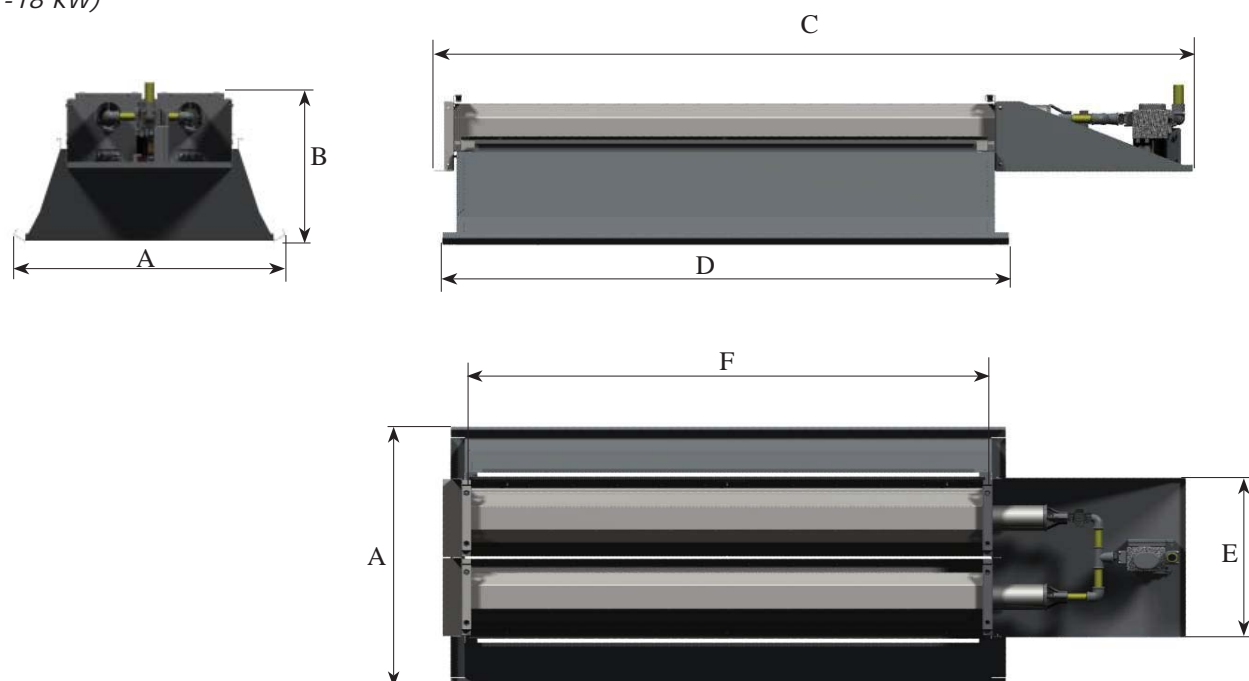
Dimensiones externas de los paneles SUNRAD para INDUSTRIA con doble unidad de radiación (22-36 kW)
